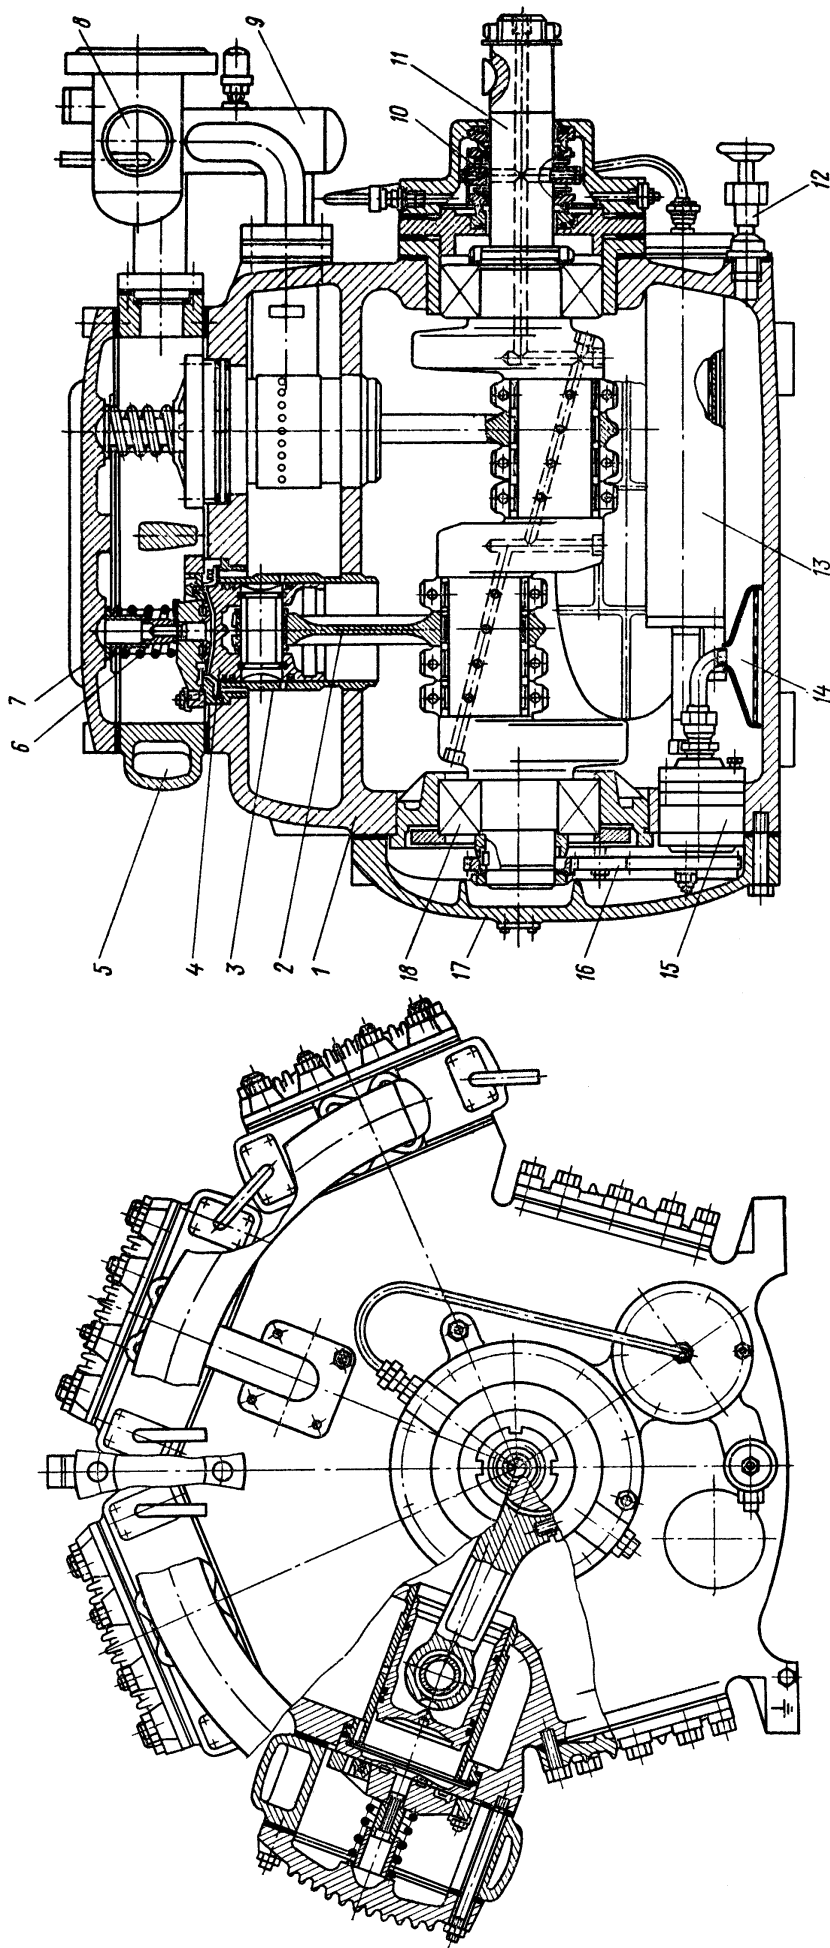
Компрессор П-220: 1 – блок-картер; 2 – шатунно-поршневая группа; 3 – гильза; 4 – клапанная группа; 5 – головка с водяной рубашкой; 6 – буферная пружина; 7 – верхняя крышка; 8 – нагнетательный коллектор; 9 – всасывающий коллектор; 10 – сальник; 11 – коленчатый вал; 12 – маслозаправочный вентиль; 13 – масляный фильтр тонкой очистки; 14 – масляный фильтр грубой очистки; 15 – масляный шестеренчатый насос; 16 – шестерни; 17 – передняя крышка; 18 – подшипник
